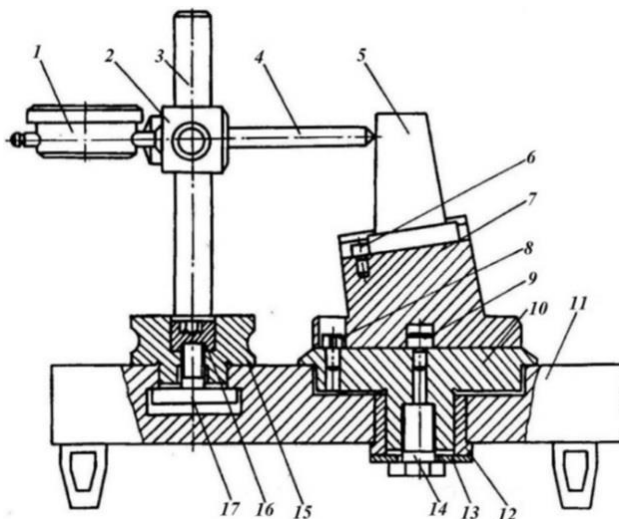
Унифицированное перенастраиваемое приспособление для контроля размеров от торца замка до входной кромки пера рабочих лопаток компрессора
